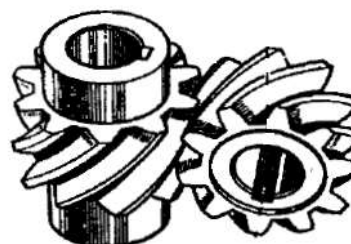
Sơ đồ bộ truyền bánh răng trụ
